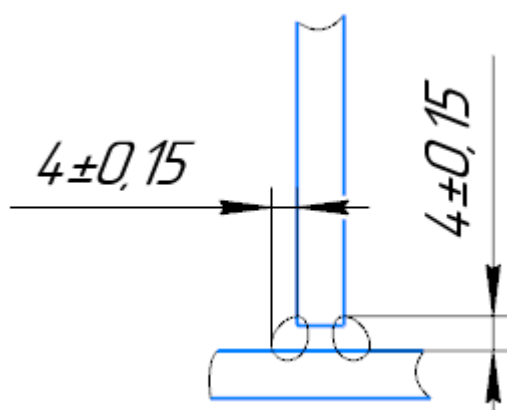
Разделка кромок и размеры сварного шва ТЗ ГОСТ 5264-80
